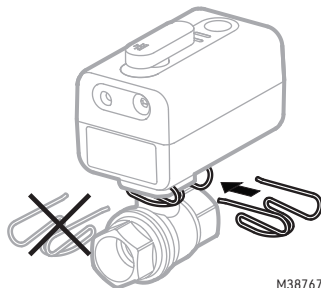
Verbinden Sie das Kugelventil mit dem Stellmotor.
